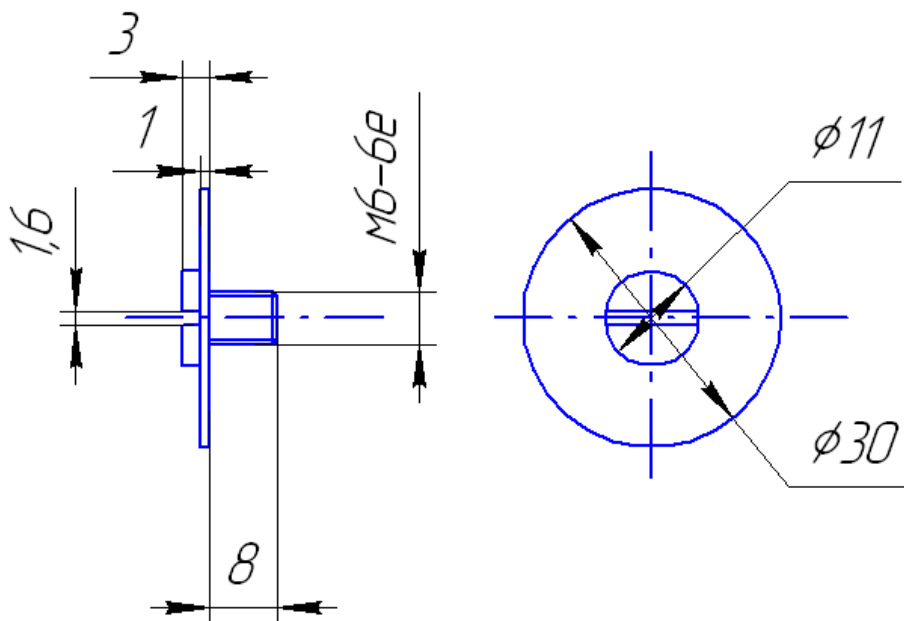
Пример 1. Чертеж детали «Фланец»
